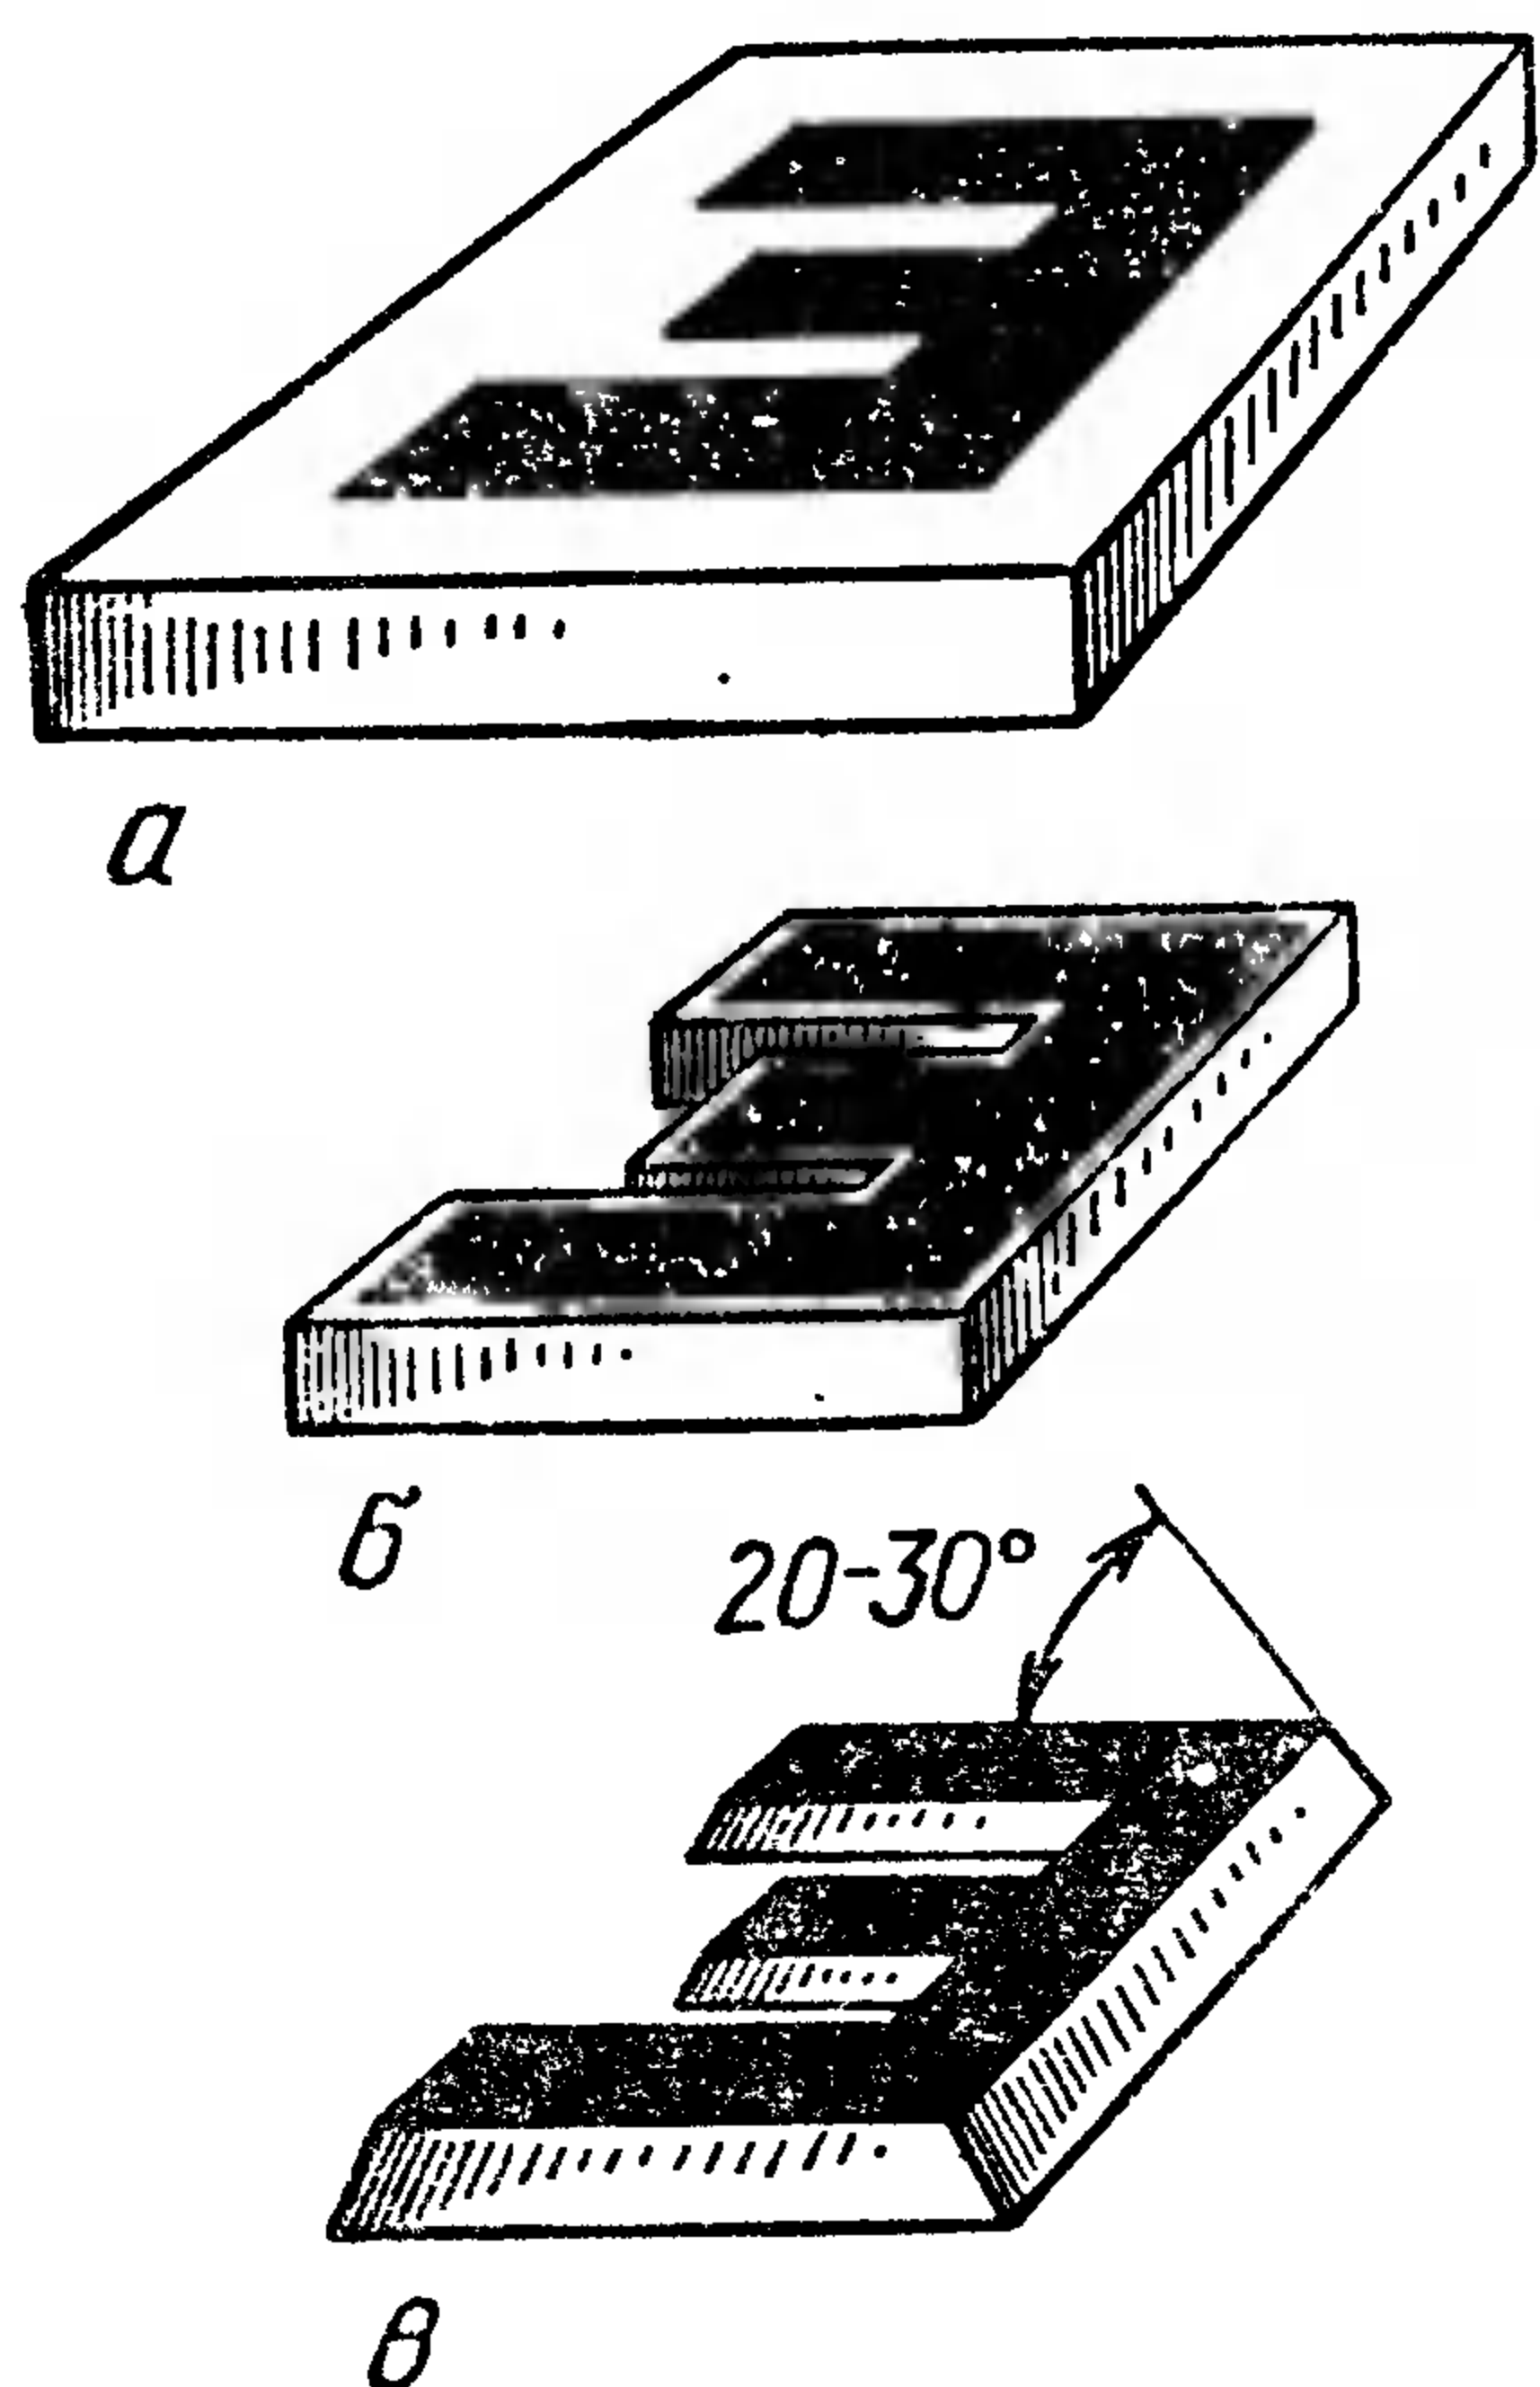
Изготовление штемпелей с литерами: а — литера, вырезанная из бумаги и наклеенная на металлическую пластинку; б — обрезка заготовки; в — обработка граней.
